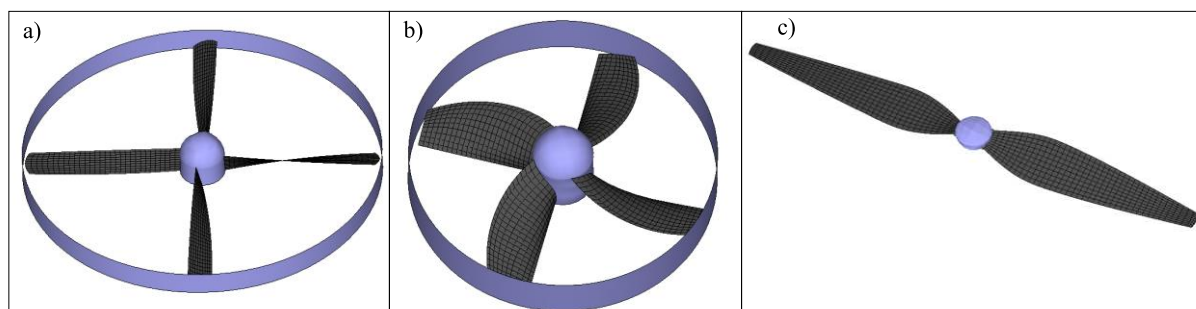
Rotores. a) Rotor 1. b) Rotor 2. c) Rotor 3.
